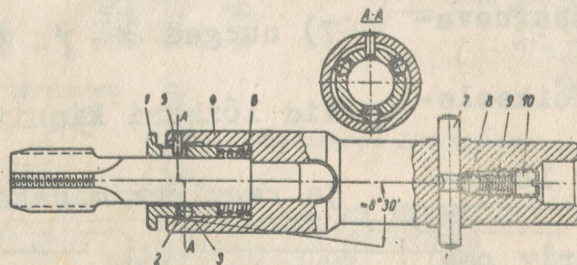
Крепление метчика в быстром патроне: 1 — корпус; 2 — пружинное кольцо; 3 — втулка; 4 — шарик; 5 — кольцо; 6 — разжимная втулка; 7 — метчик.
